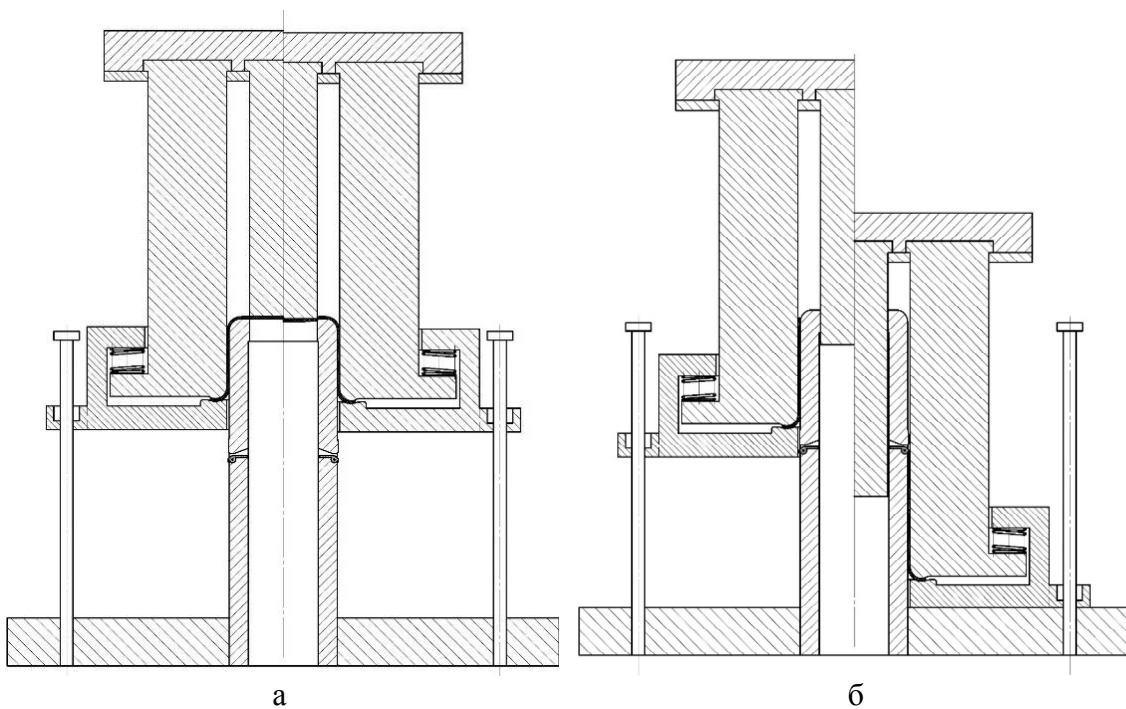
Стадии штамповки: а — вытяжки и пробивки, б — отгибки и протяжки
